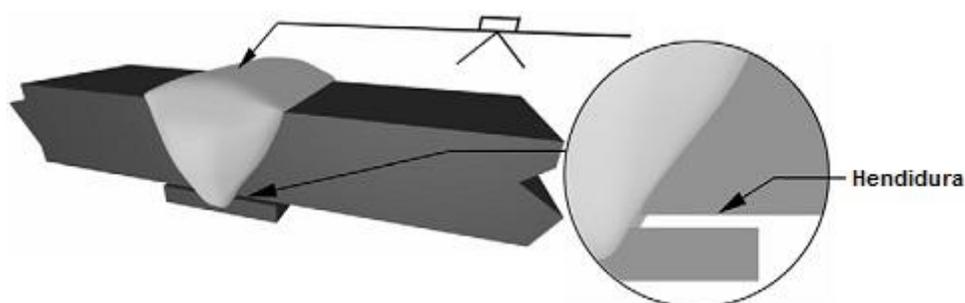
Unión por soldadura de tipo 2.
